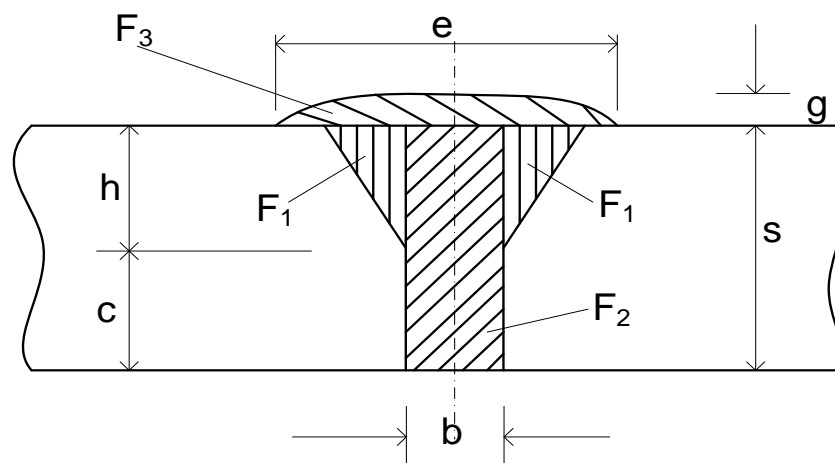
Схема стыкового соединения с разделкой кромок
